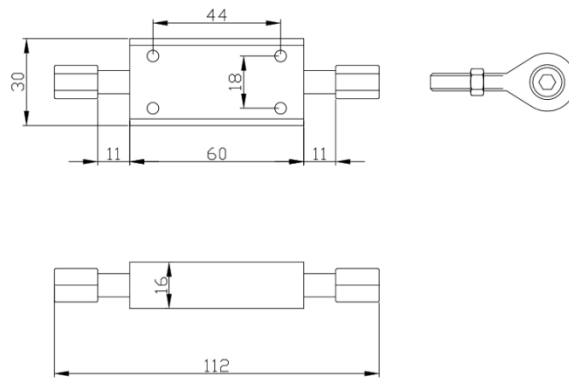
Dimensiones Captador de Posición CSEM-C-01
